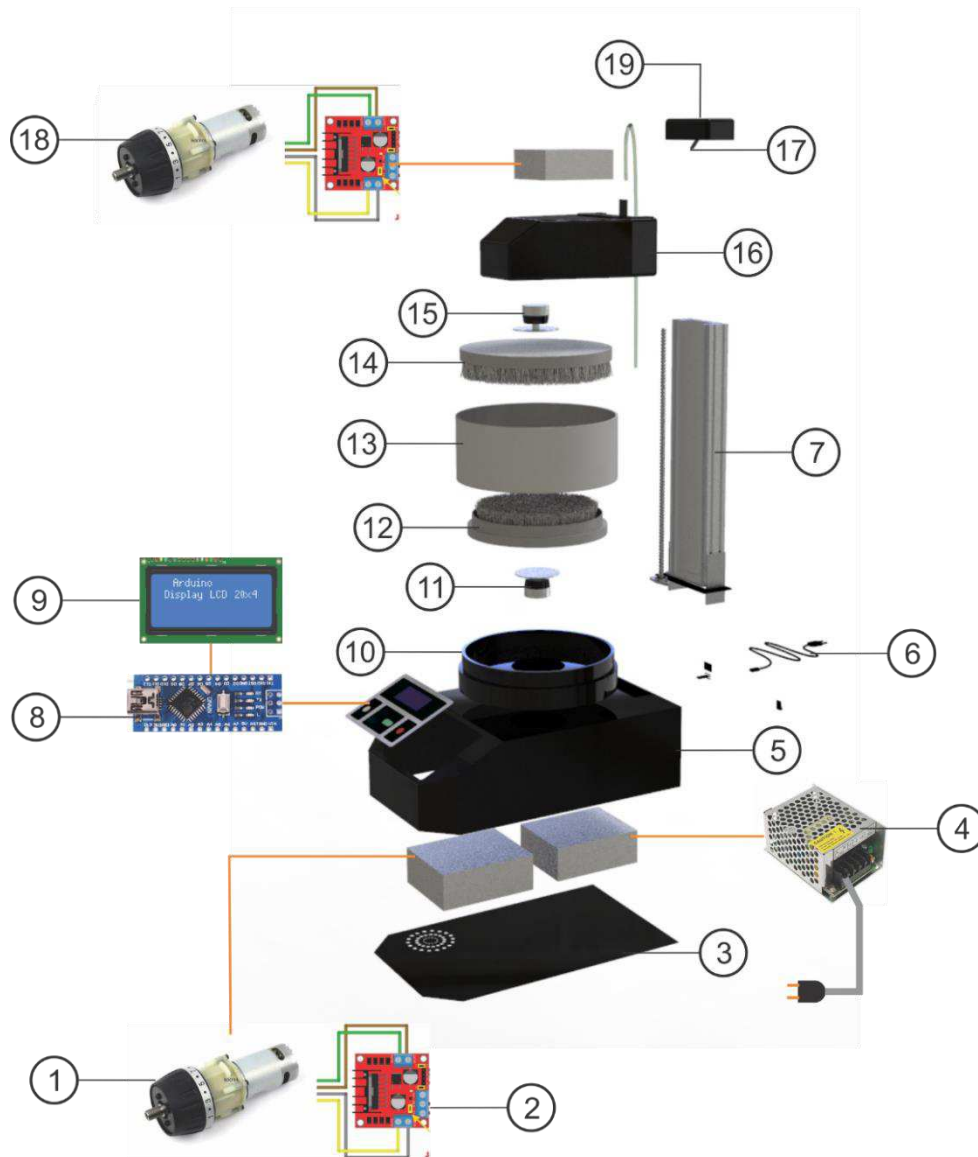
Perspectiva explodida de partes e componentes do despeliculador
